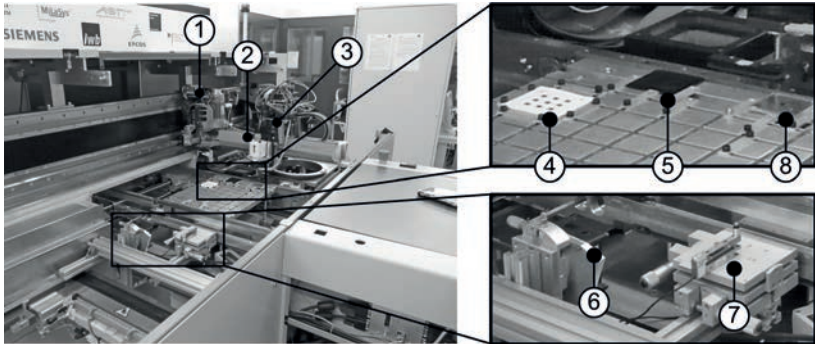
Prototypischer Aufbau einer Montageanlage auf Basis des Siemens Si-Place D2 Bestückautomaten mit integriertem Ultraschallvakuumgreifer. 1. Portalroboter, 2. Ultraschallvakuumgreifer, 3. Bestückkopf, 4. Bauteilträger, 5. Waffle-Pack, 6. Laser-Triangulationsensor (im Bild ist dieser nicht am Bestückkopf montiert, da er zum Zeitpunkt der Bildaufnahme zur Verifikation des Luftspaltreglers eingesetzt wurde), 7. Kraftsensor, 8. Gel-Pack.
